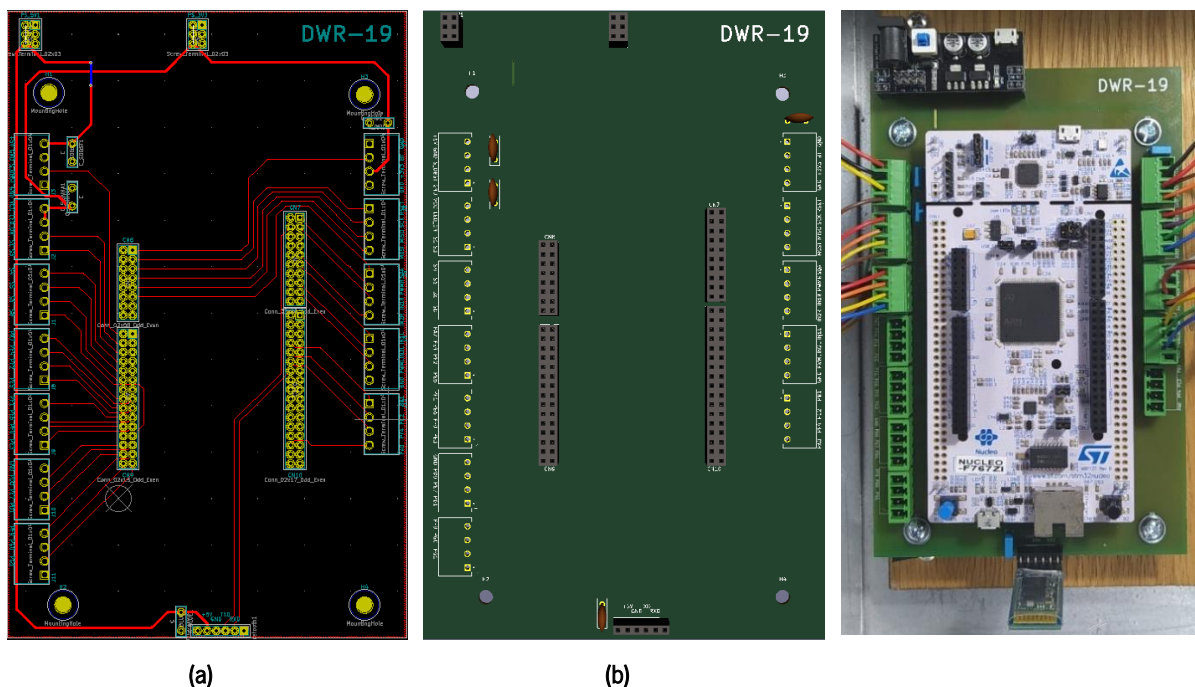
Shield* desenvolvida: (a) *Layout* da PCB desenvolvida em KiCad; (b) Imagem 3D KiCad (c) PCB já totalmente montada.
